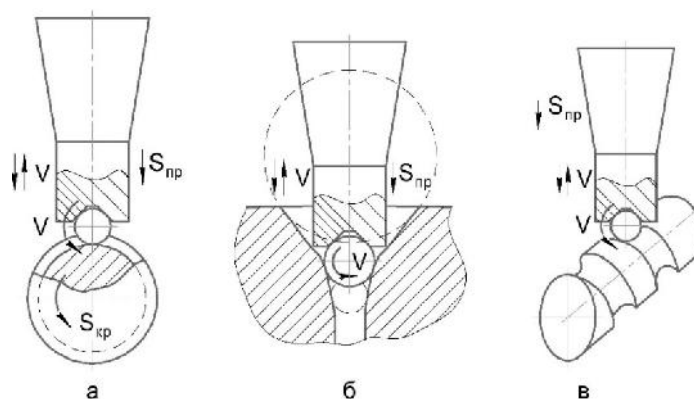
Схемы обработки сложных поверхностей незакрепленными инструментами [1].
